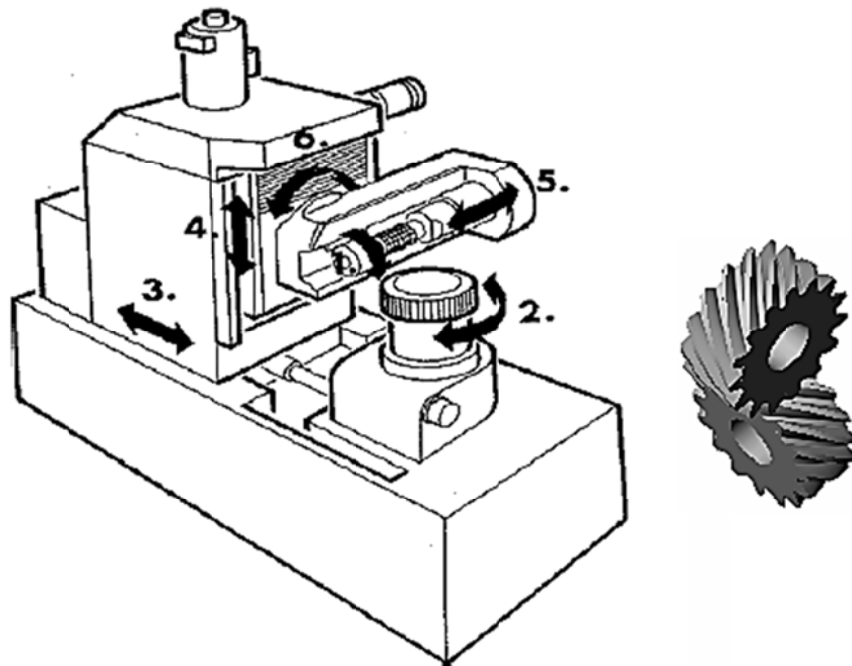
Schéma d'une machine à tailler les engrenages [13]
